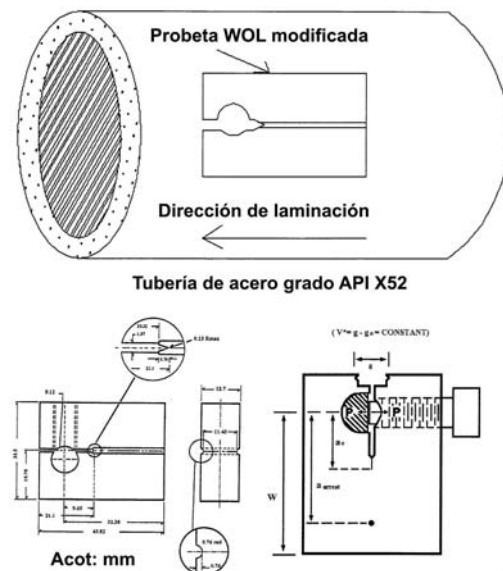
Probeta MWOL modificada, dimensiones y dirección de corte-maquinado.
